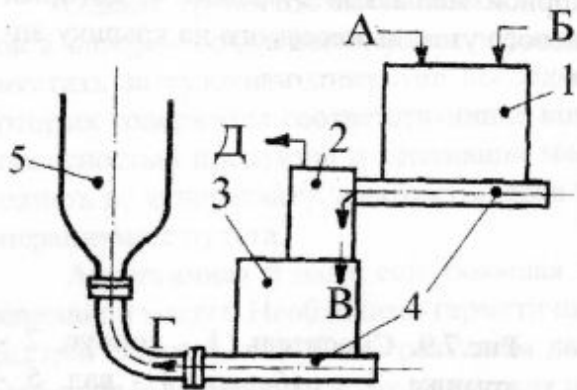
Смеситель типа СНД. 1 - верхний мешатель, 2 - вакуумная камера, 3 - нижний мешатель, 4 - разгрузочный шнек, 5 - корпус ракетного двигателя; А, Б - подача компонентов, В - подача шнуров, Г - подача топливной массы, Д - отсос воздуха
